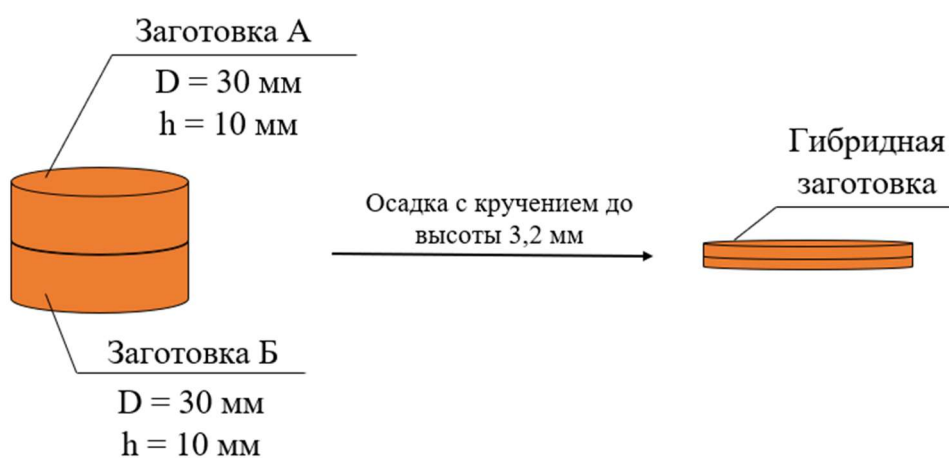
Схема осадки образцов из медного сплава БрХ0,8
